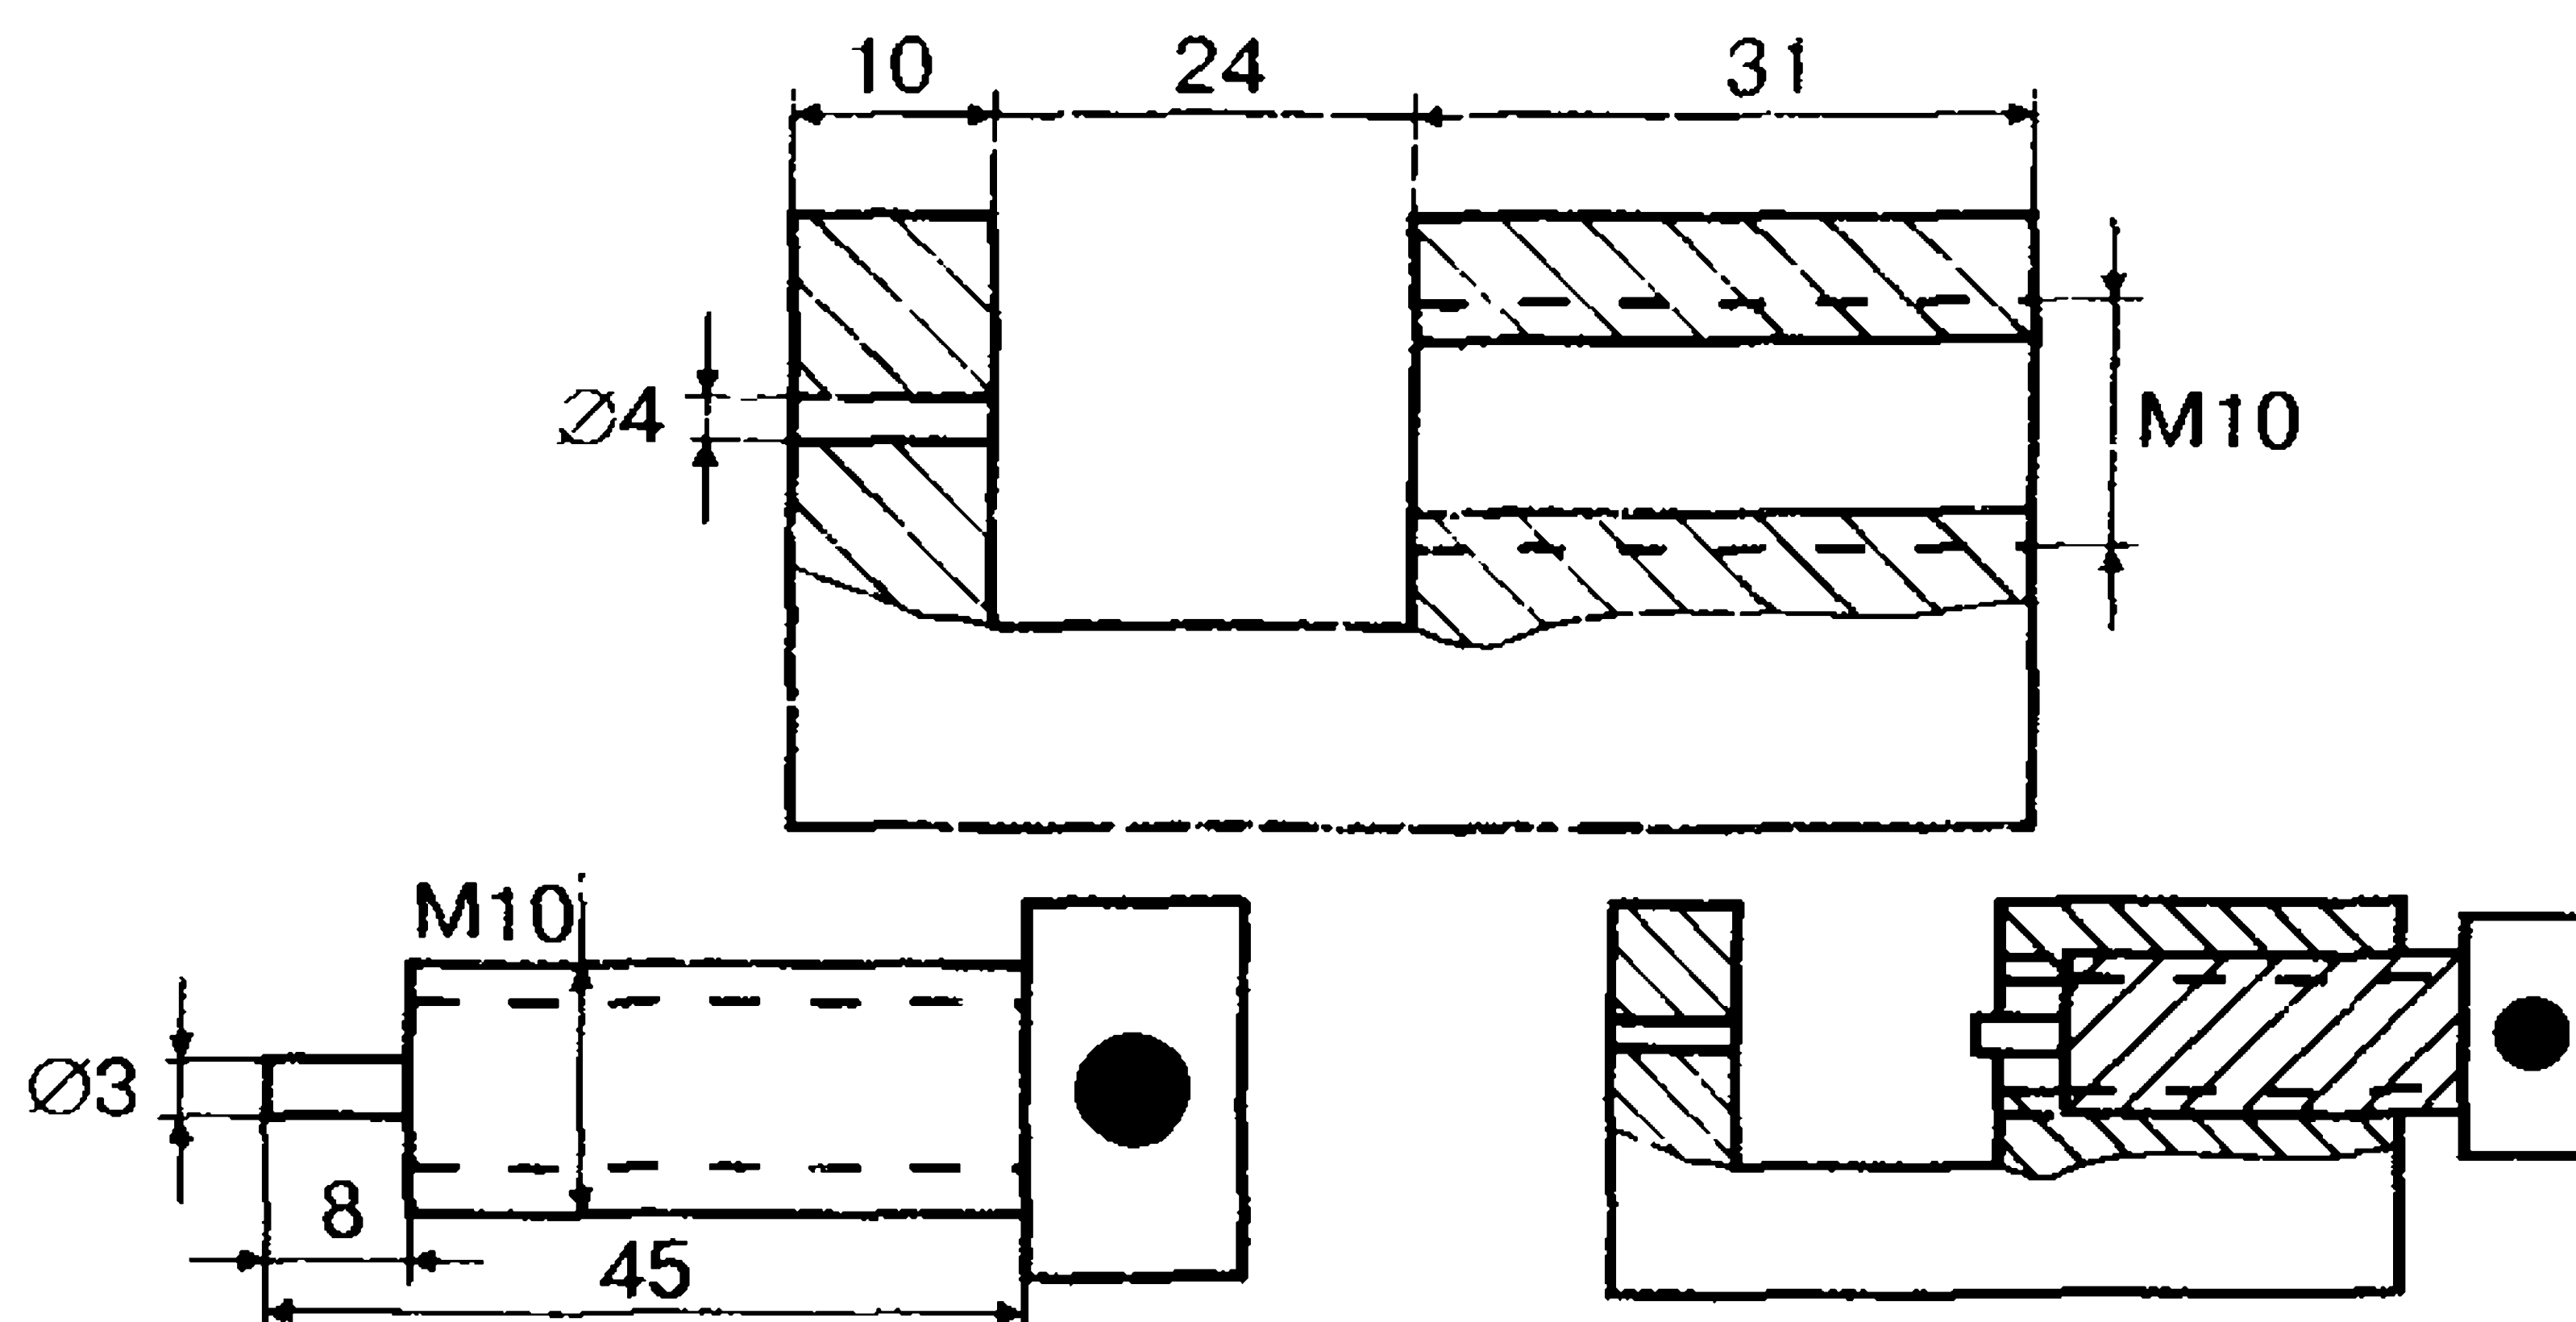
Съемник для выпрессовки соединительных пальцев цепи
